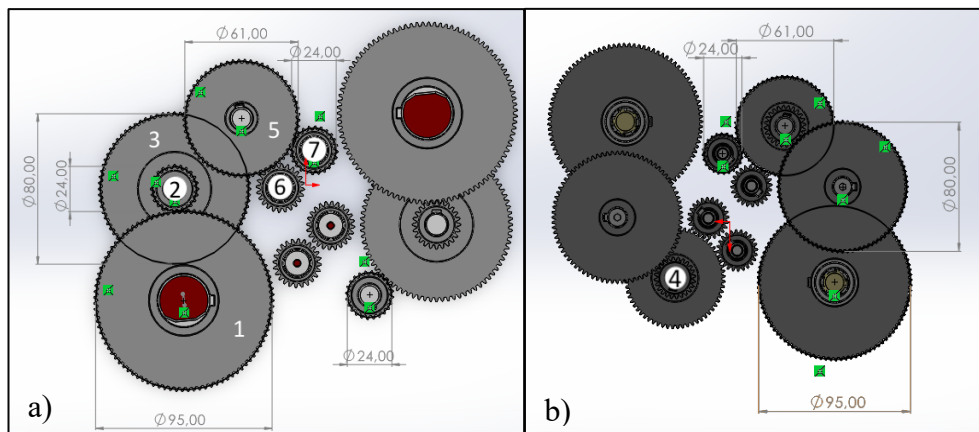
Sistema de engrenagens com medidas: a) Vista de topo e b) Vista de baixo.
